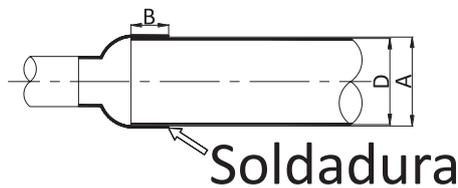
Orientación de tuberías durante la soldadura
